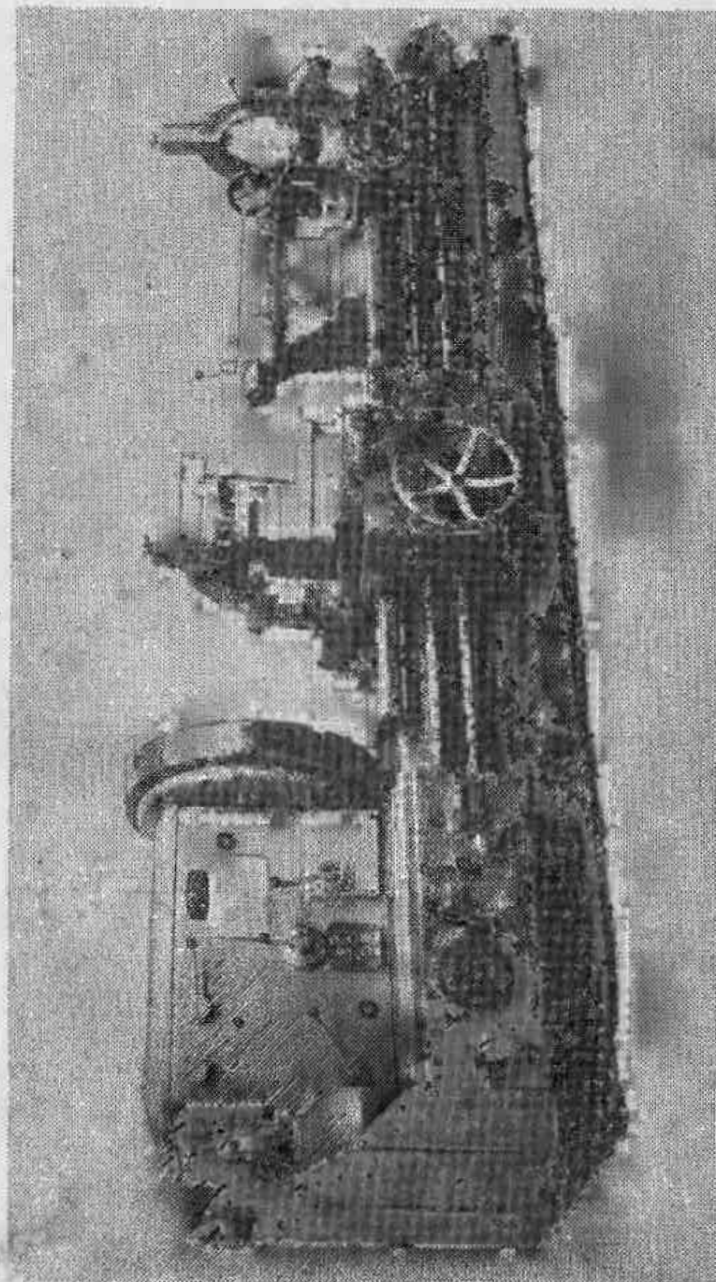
Универсальный токарно-винторезный станок модели 165.
